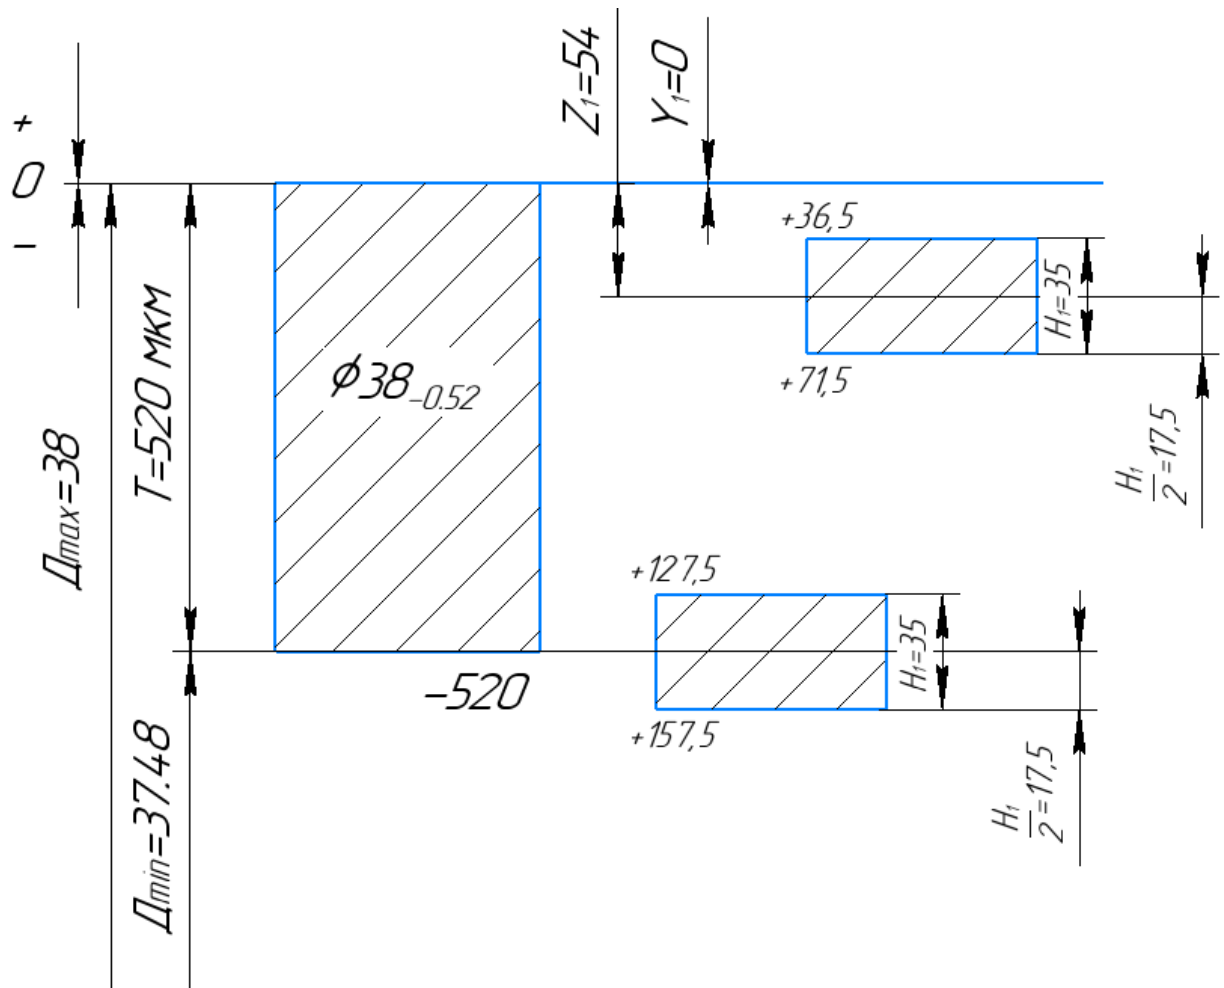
Схема полів допусків калібрів-скоб для контролю внутрішньої циліндричної поверхні втулки $\phi 38_{-0.52}$
